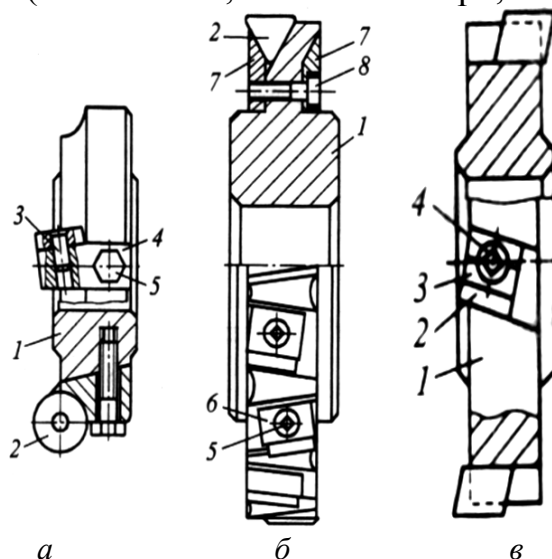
Сборные дисковые фрезы с открытыми базами для СМП
